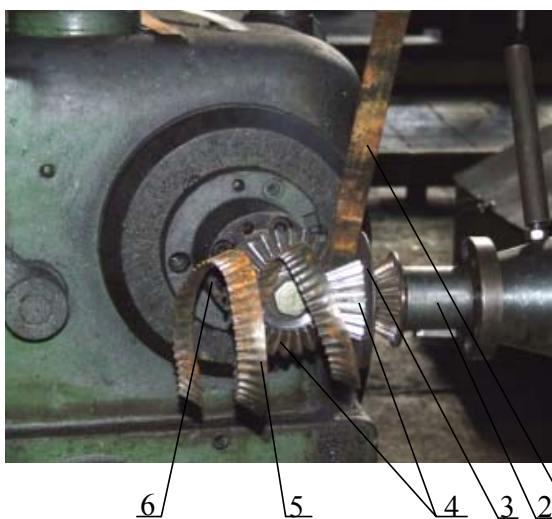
Технологічний процес формоутворення ГГЗ парою ортогональних формувальних інструментів ($\alpha=90^\circ$) на обкатному верстаті: 1 – заготовка; 2 – ведучий шпиндель; 3 – упорне кільце; 4 – пара конічних зубчастих коліс; 5 – гвинтова гофрована спіраль; 6 – ведений шпиндель
